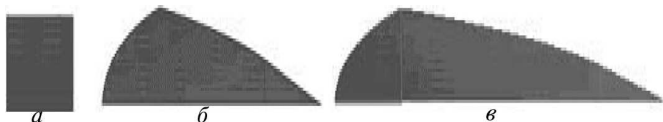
Изображения смоделированных поверхностей контакта (вид сверху) РП ШК с заготовкой:
